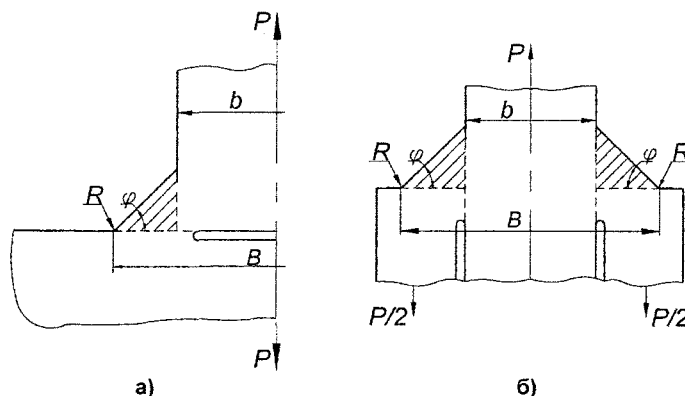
Расчетная схема таврового сварного соединения (а), нахлесточного сварного соединения (б)
